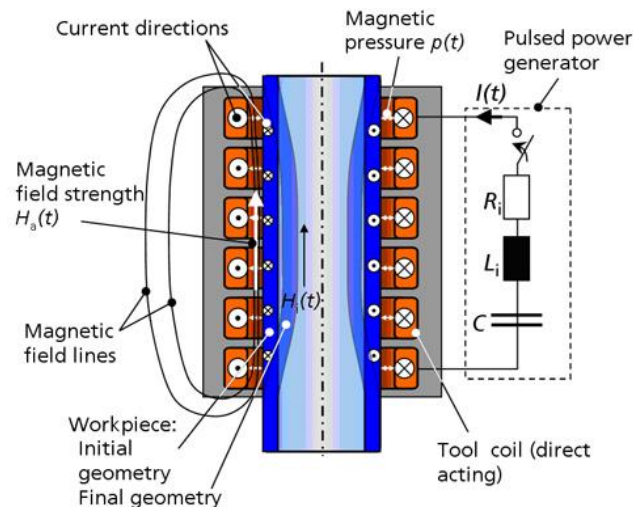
schematizzazione del processo di electromagnetic forming.
